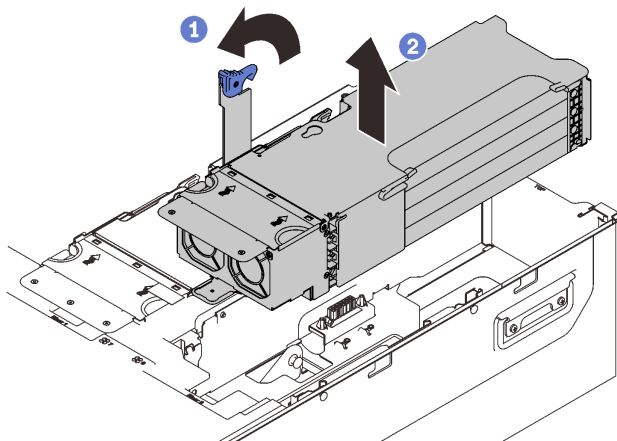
Removendo o compartimento de placa riser PCIe 4U
